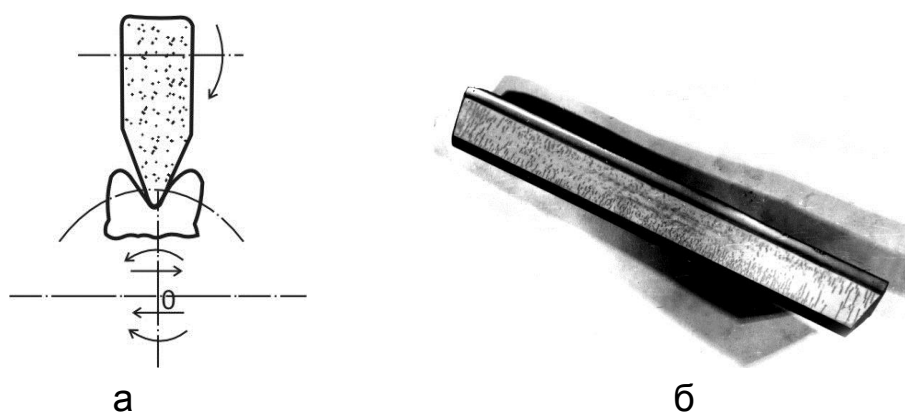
Схема обработки зубчатого колеса на зубошлифовальном станке НАИЛС (5831) (а); шлифовальные трещины на зубе (б)
